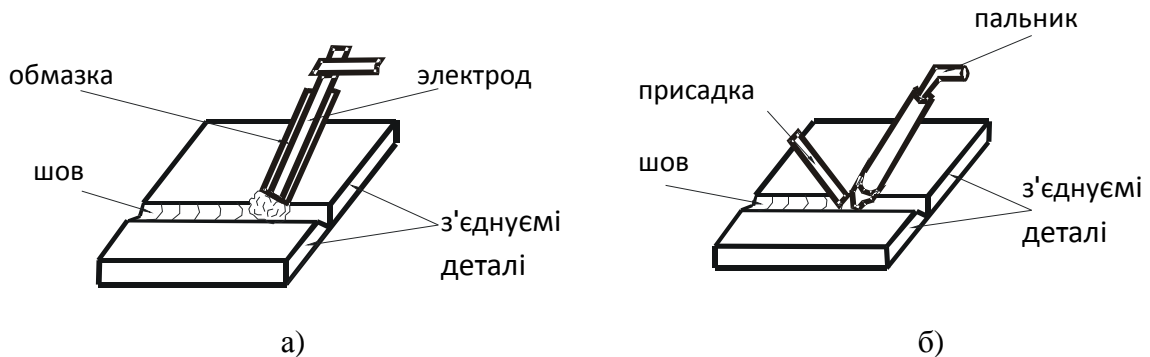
Зварювання: а – електричне зварювання (дугове зварювання); б – газове зварювання
